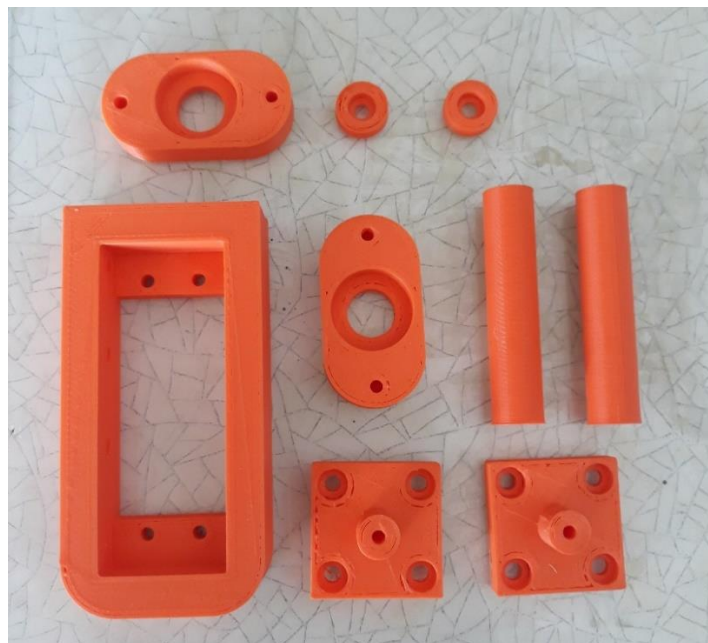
Надруковані деталі рукоятки робота-маніпулятора
